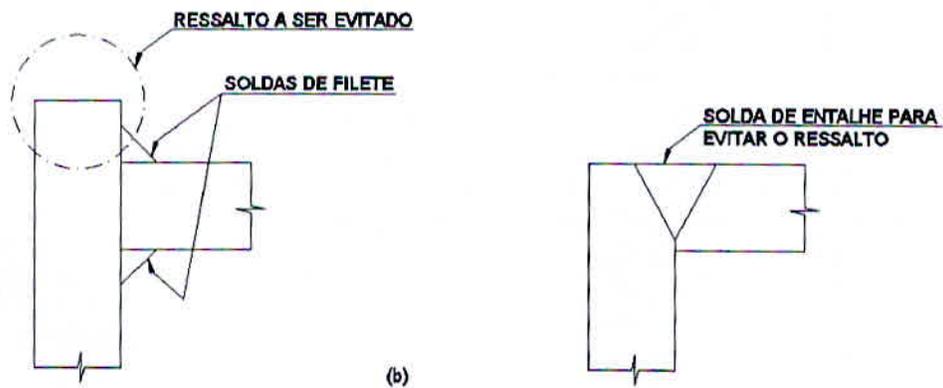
Soldas de Entalhe. Fonte: Autor
